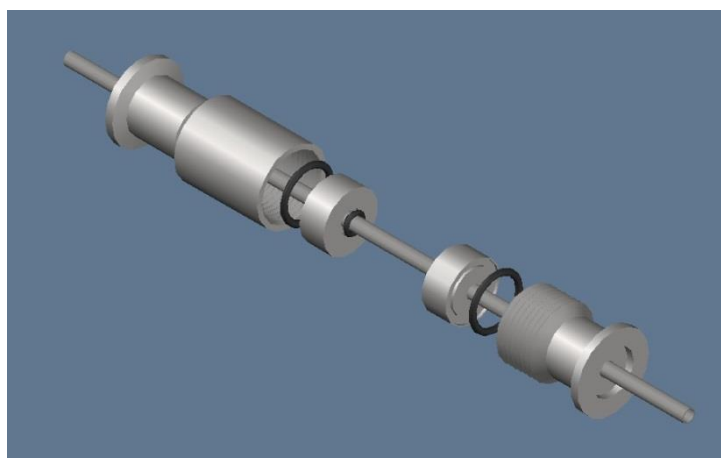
Desenho em AutoCAD 2013 da vista expandida do conjunto completo montado.
